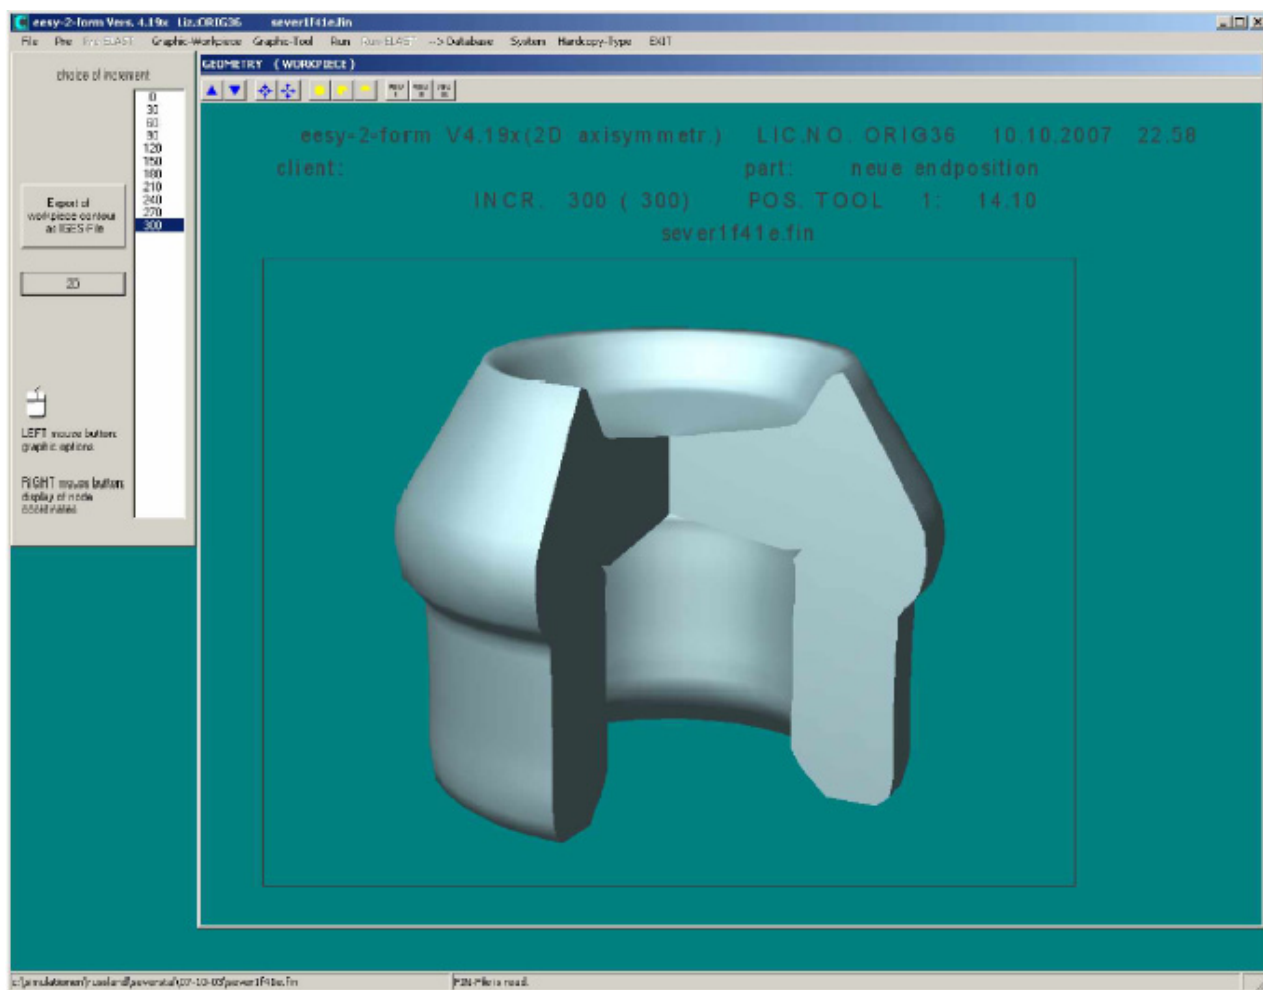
4-й переход штамповки гайки с внутренним дефектом
